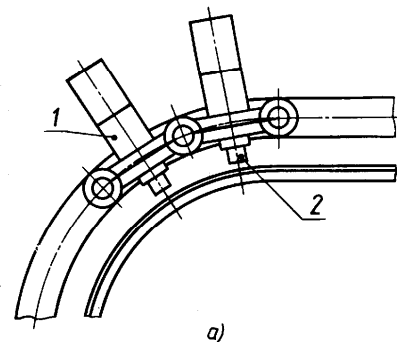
Универсальный стенд для сварки секций крыш
